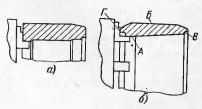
Изготовление бандажного кольца турбогенераторов ТВВ-165-2, ТВФ-100-2 на токарном станке.
